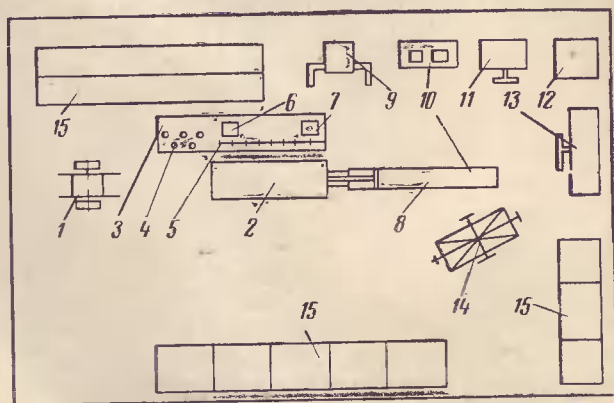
Технологическая линия для обработки и заготовки трубопроводов из пластмассовых труб.
